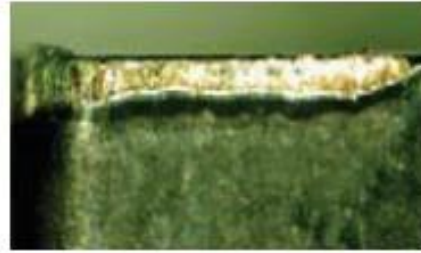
Знос головної задньої поверхні ЗНБП токарного різця
